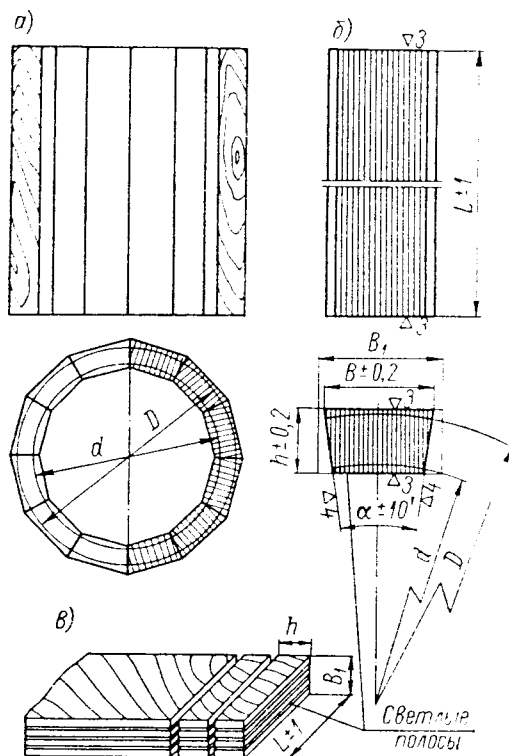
Заготовка для втулки из древесластика: а — заготовка для втулки; б — сегмент заготовки; в — схема разрезки плиты на сегменты
